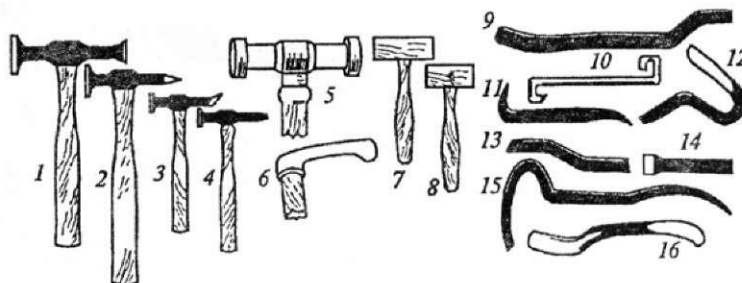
Набор инструментов для удаления вмятин: 1-6 - молотки; 7 и 8 - киянки; 9-19 - оправки
